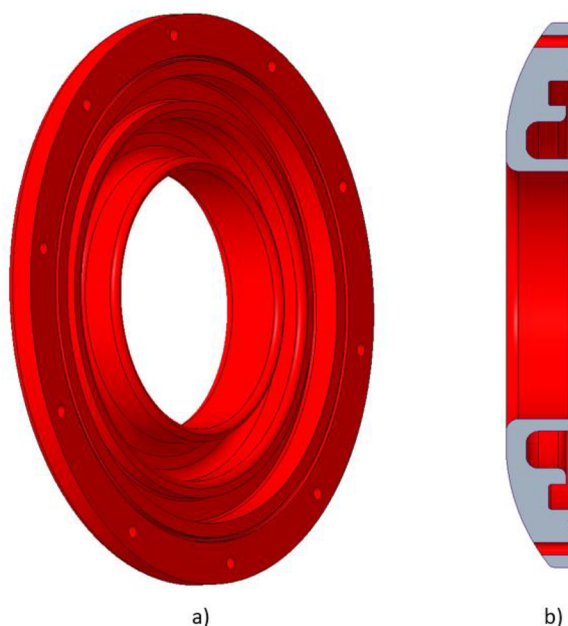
Pryžový doraz a) v obecném pohledu b) v řezu
